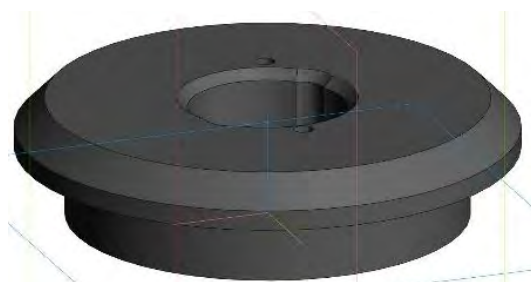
3D модель корпуса прессовой оснастки для прессования дугового канала времязадающего кольца ПИМа
